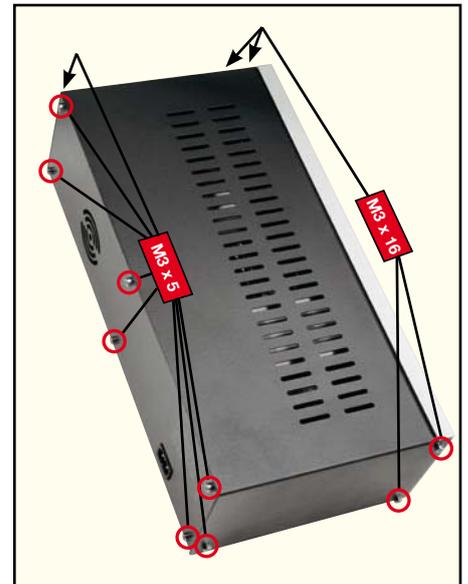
Montage des Gehäusedeckels mit Inbusschrauben
